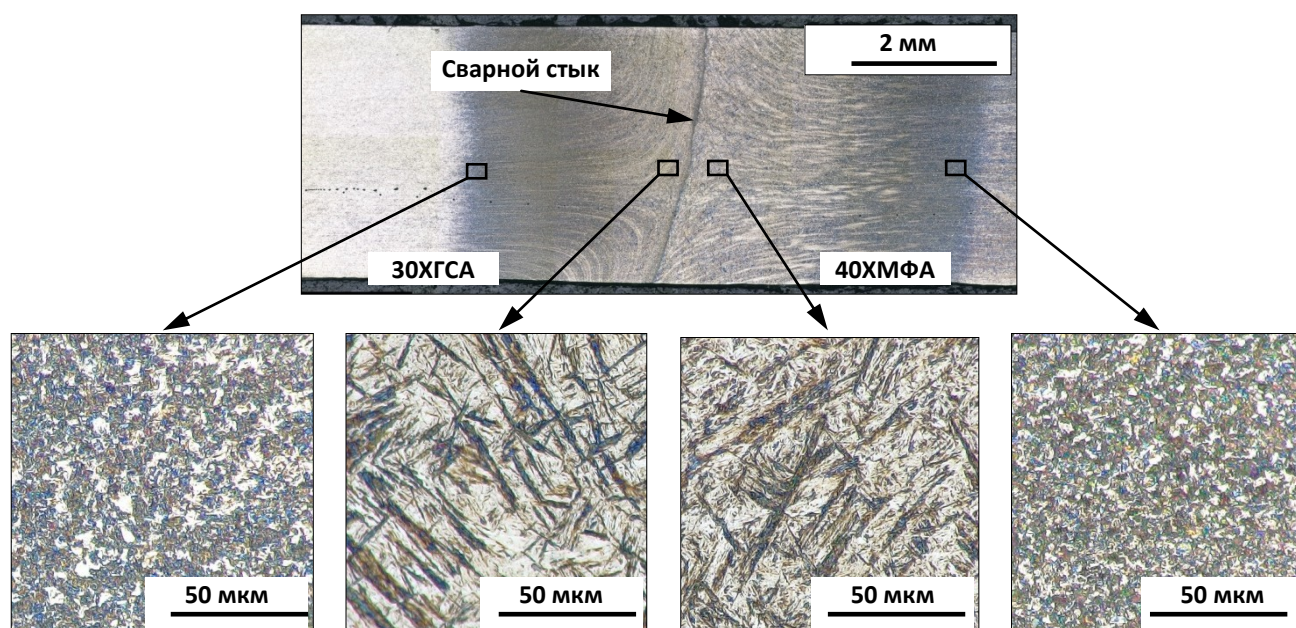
Макро- и микроструктура сварного соединения сталей 30ХГСА и 40ХМФА, полученная ротационной сваркой трением (режим № 2)
